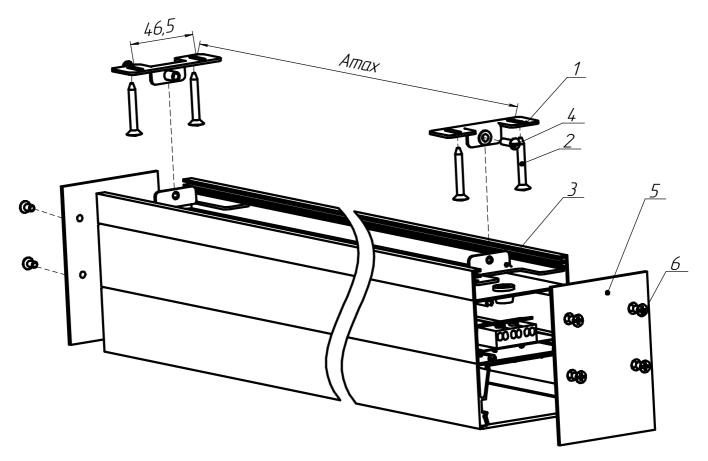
Схема крепления светильников к потолку 1 - скоба, 2 - саморез 4.5х30, 3 - скоба, 4 - винт М4х12, 5 - торцевая крышка, 6 - саморез
